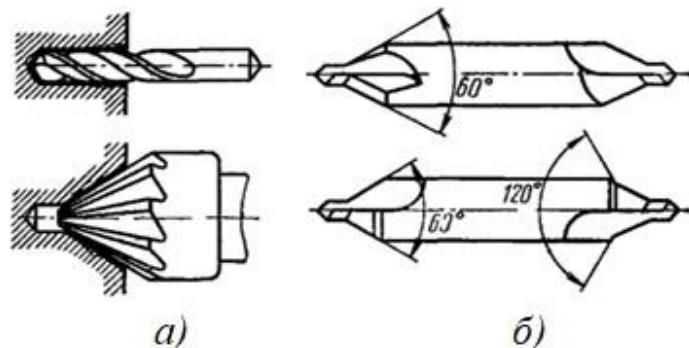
Процес центрування та комбіновані центрувальні свердла
